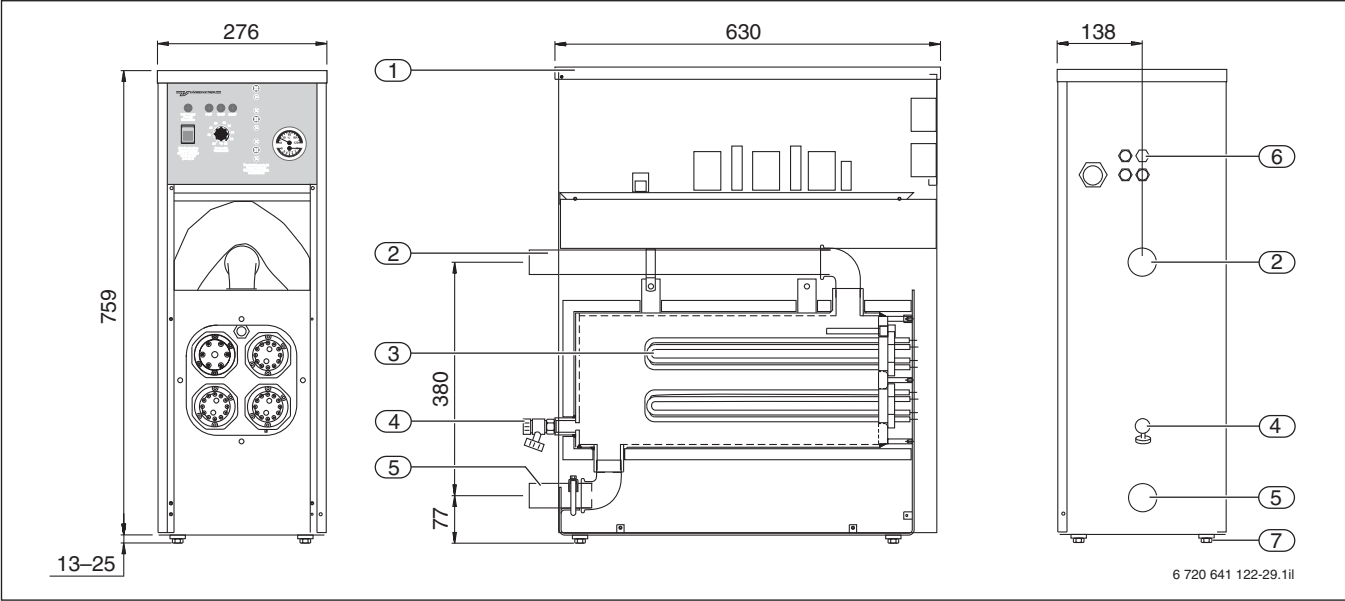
Abmessungen elektrischer Zuheizer EK 26 E (Maße in mm)
